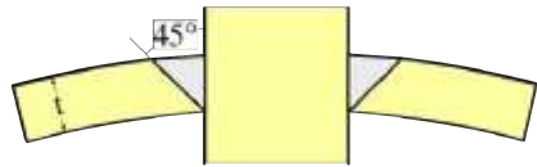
Geometría de diseño típica para los cordones de la unión soldada chapa-perfil tubular.
